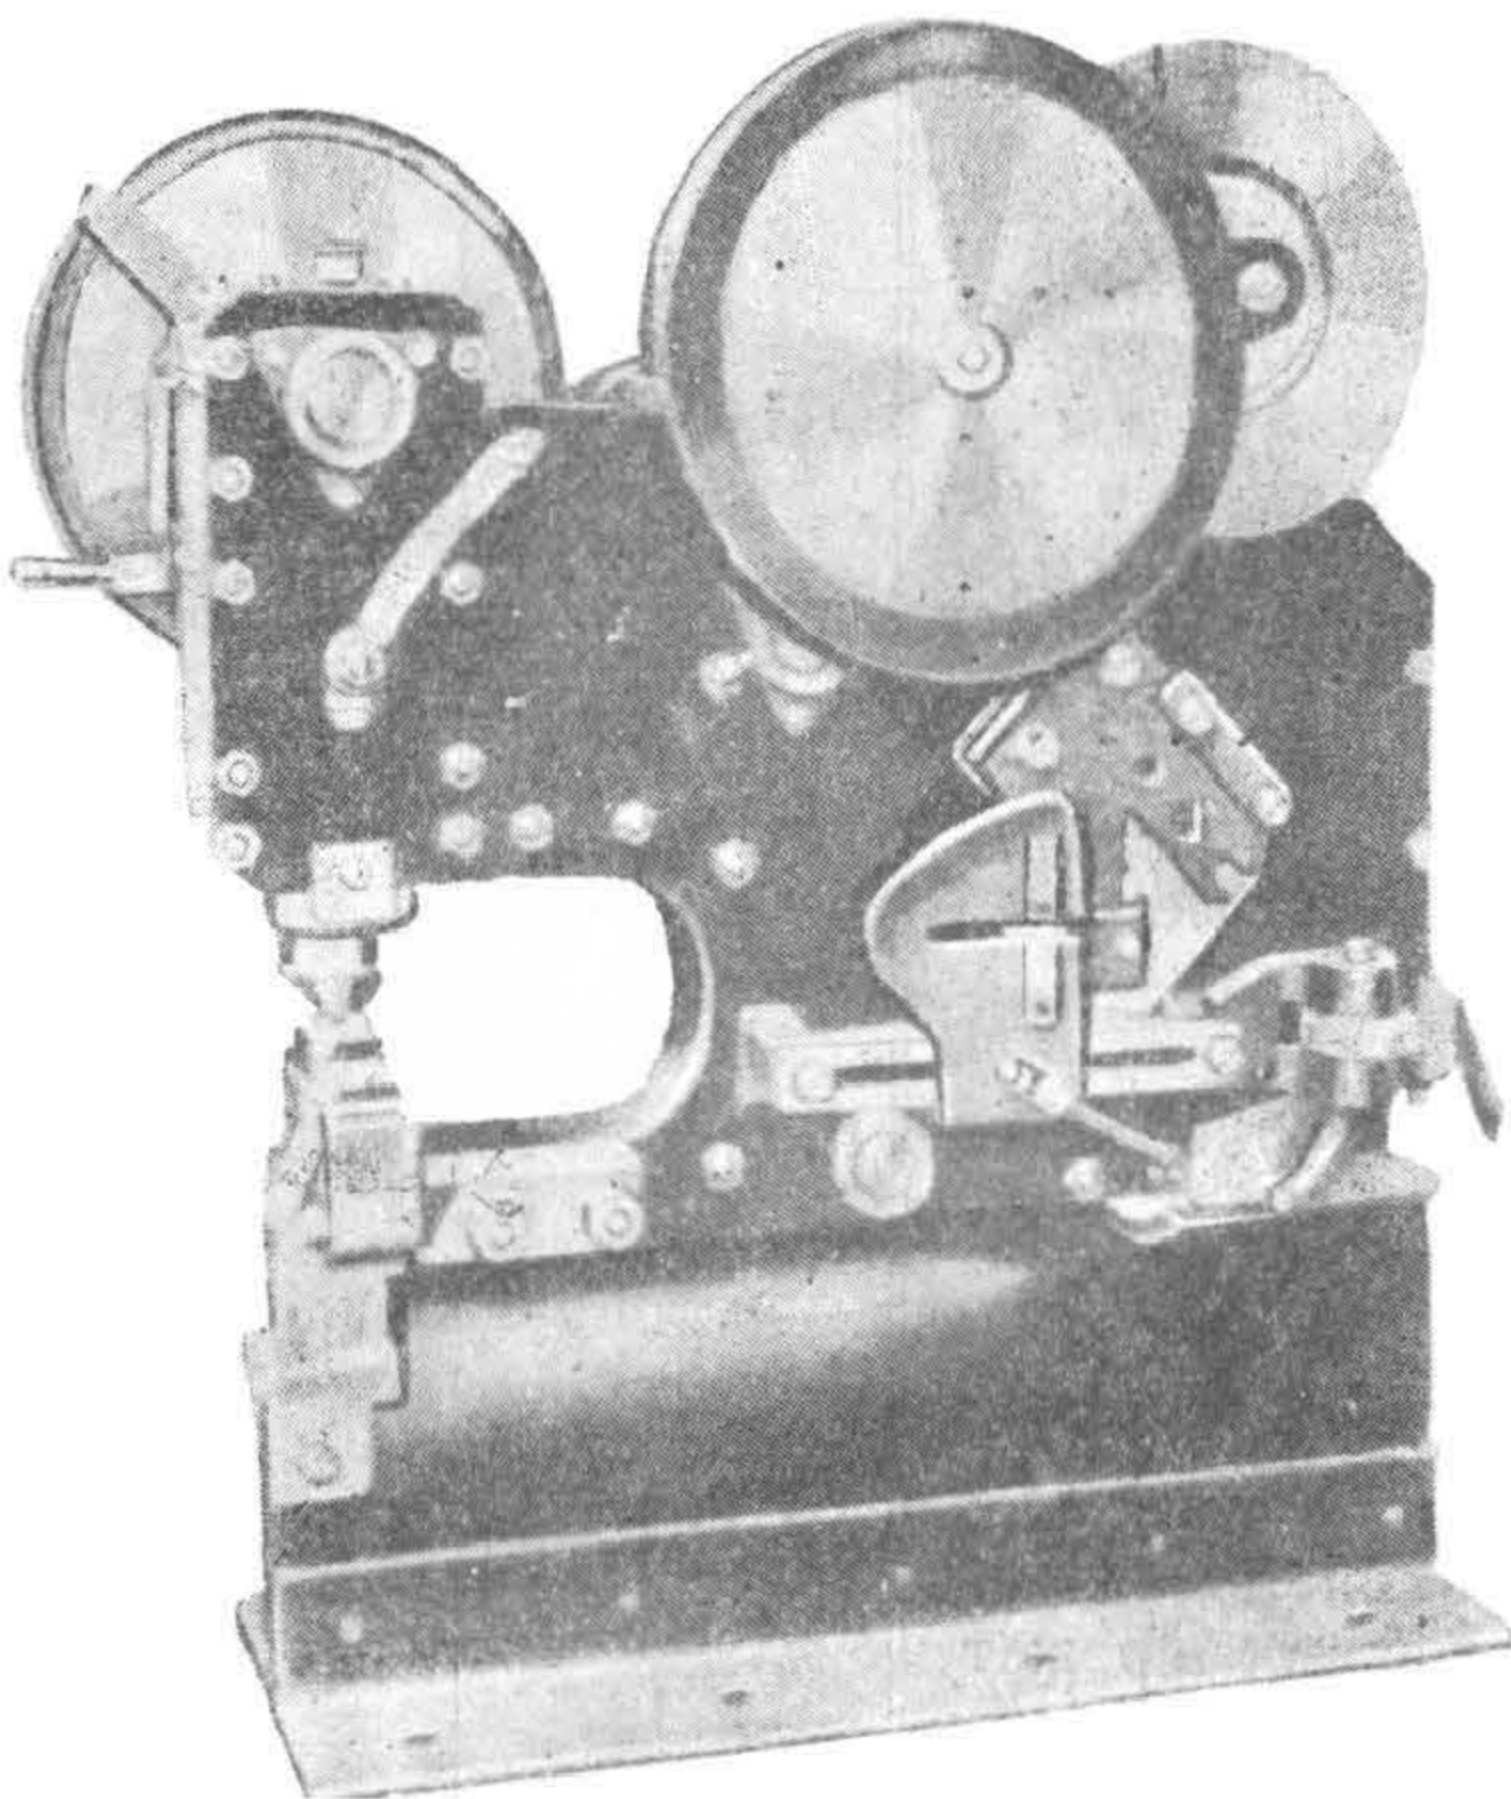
Пресс для пробивки дыр с суппортом для резки профильного материала.
